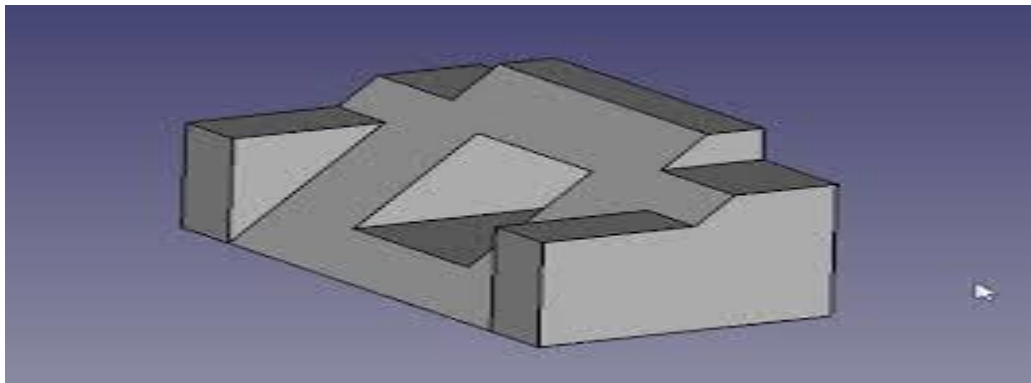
Exemple de pièce modélisée dans Part Design.
